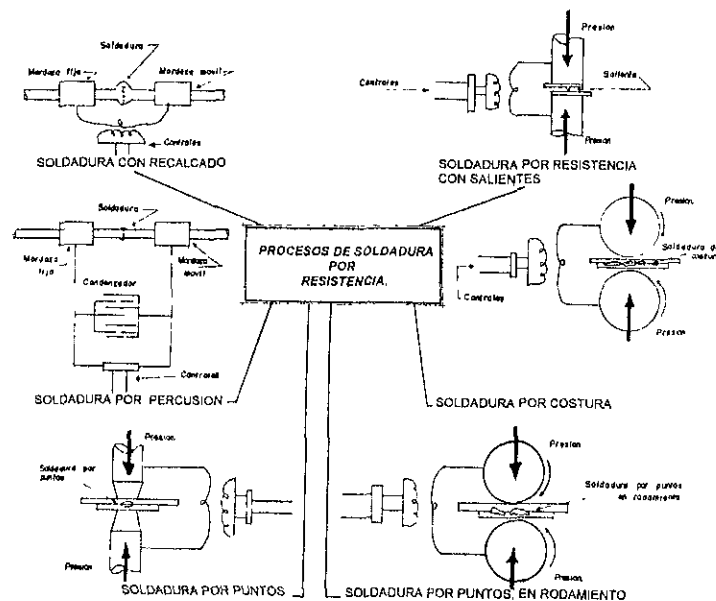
Procesos de soldadura por resistencia.
